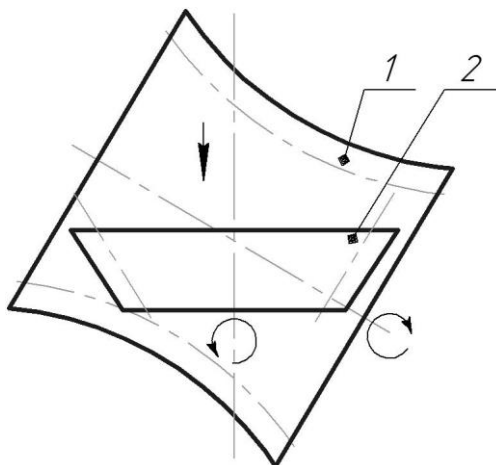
Схема изготовления квазигиперболических зубчатых колес
